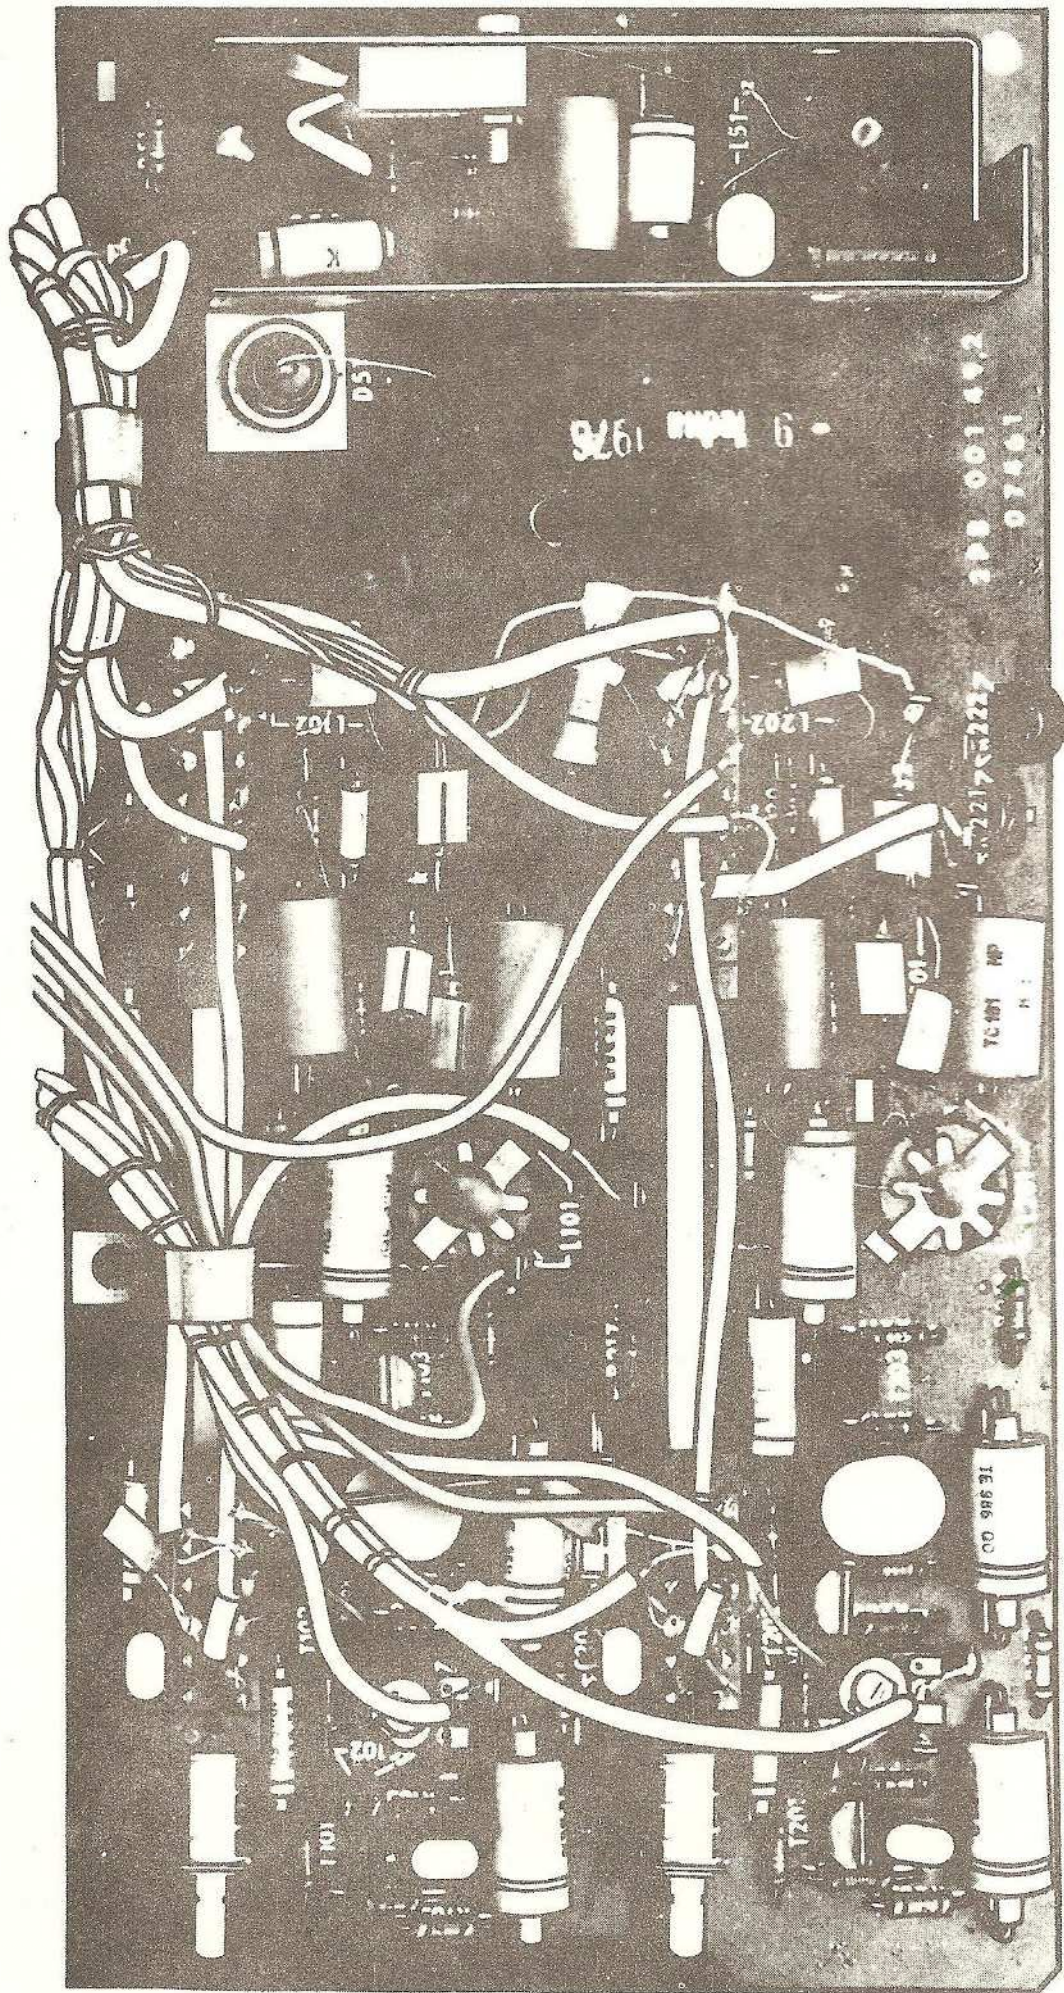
Deska korekčního zesilovače H101, B100A (ze strany spojů)
